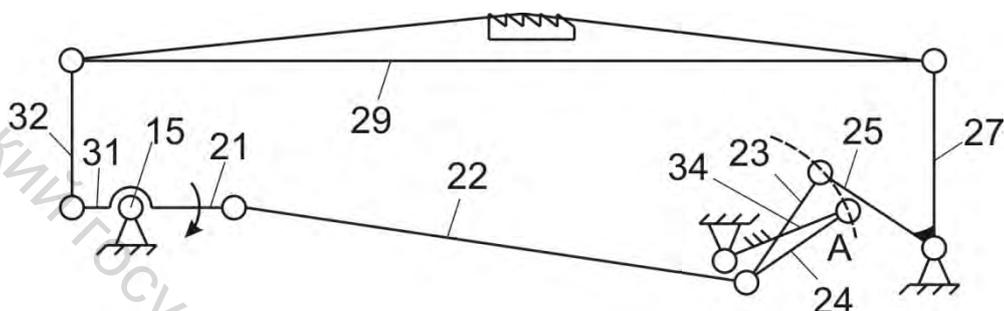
Кинематическая схема механизма двигателя материала
